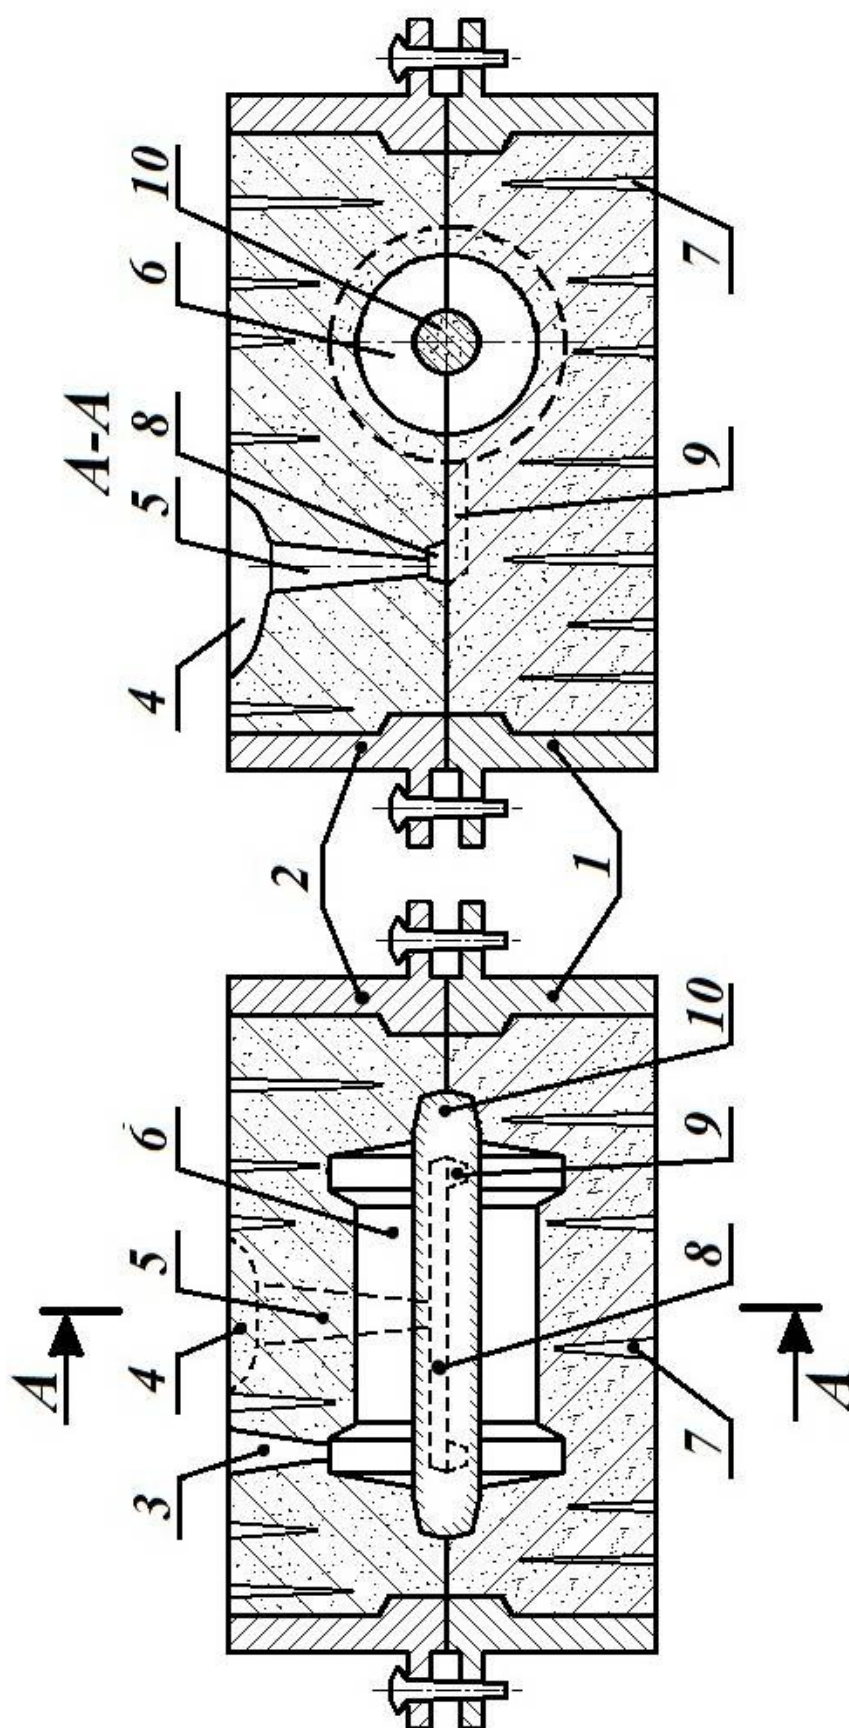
Эскиз разреза песчаной формы для отливки стальной втулки:
